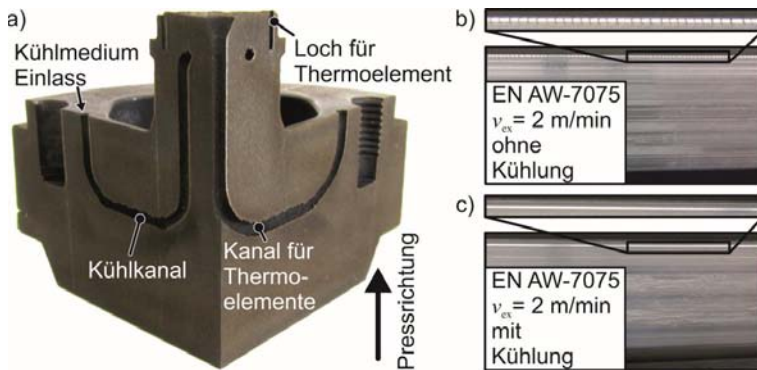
a) Strangpresswerkzeug mit konturnahen Kühlkanälen (Hölker und Tekkaya, 2016; Hölker, 2014), b) Heißrisse beim Strangpressen ohne Kühlung und c) keine Heißrisse bei Einsatz des gekühlten Werkzeugs (Hölker, 2014)
